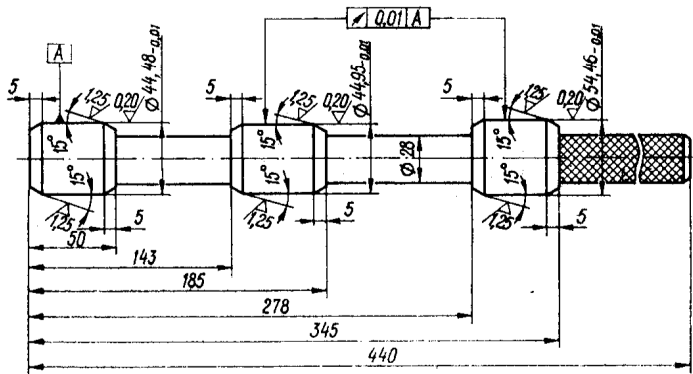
Оправка для проверки соосности подшипников распределительного вала
